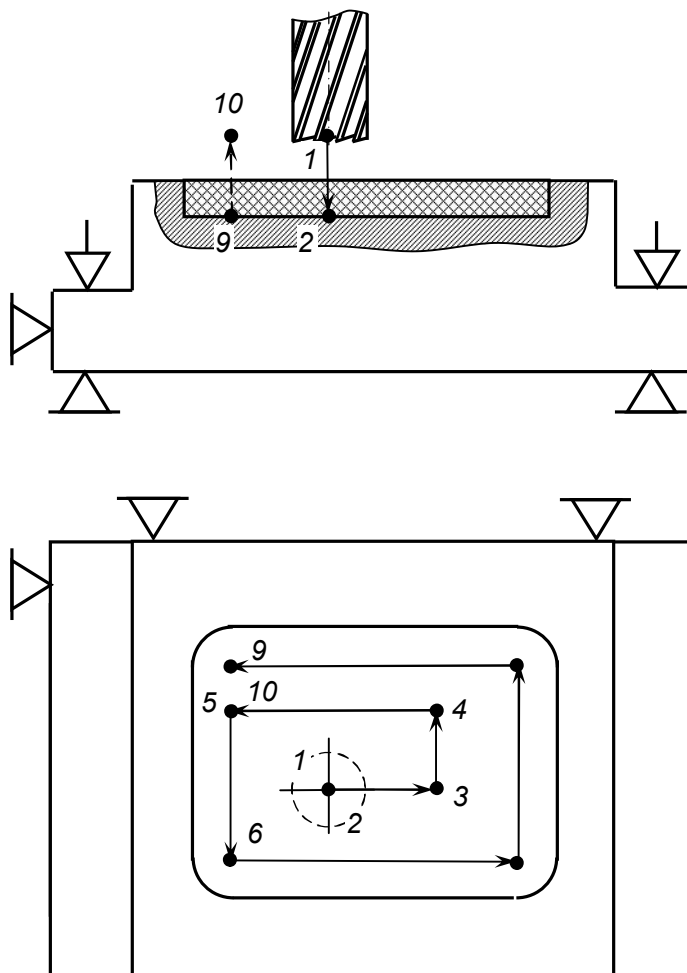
Схема фрезерної обробки закритої зони
